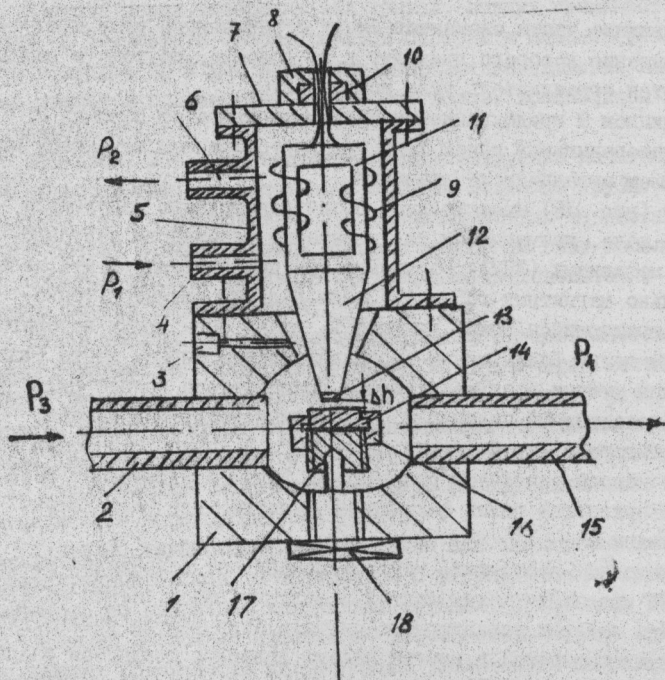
Конструкция установки для ультразвуковой гидроабразивной обработки детали
